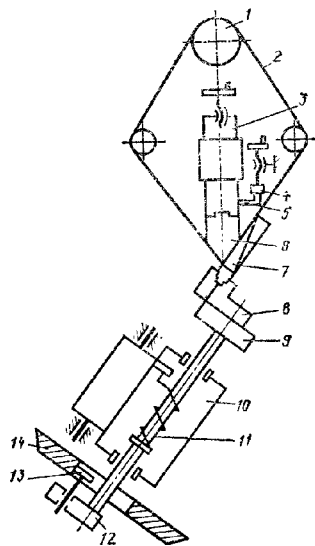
Кинематическая схема шлифовально-полировального станка модели 3B24:
